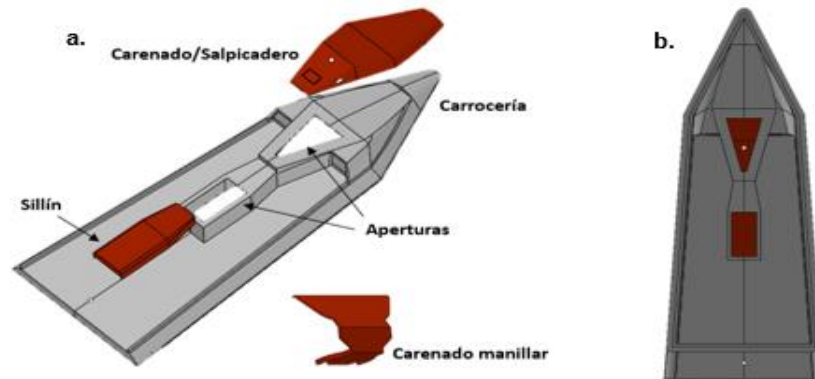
Carrocería del diseño final. a) vista explosionada, b) vista inferior (Fuente: elaboración propia).
